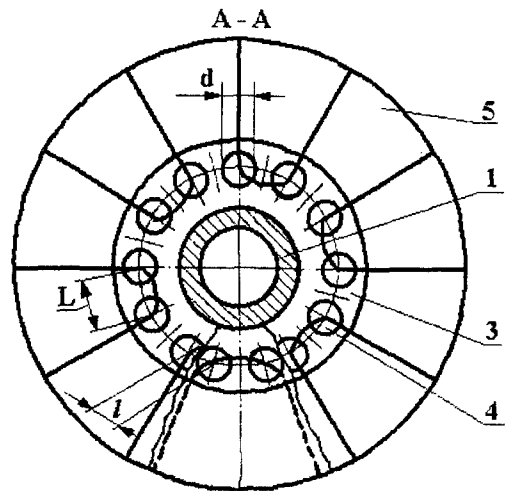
Схема сборки дисков с проволочными пучками (иглофрезы)
